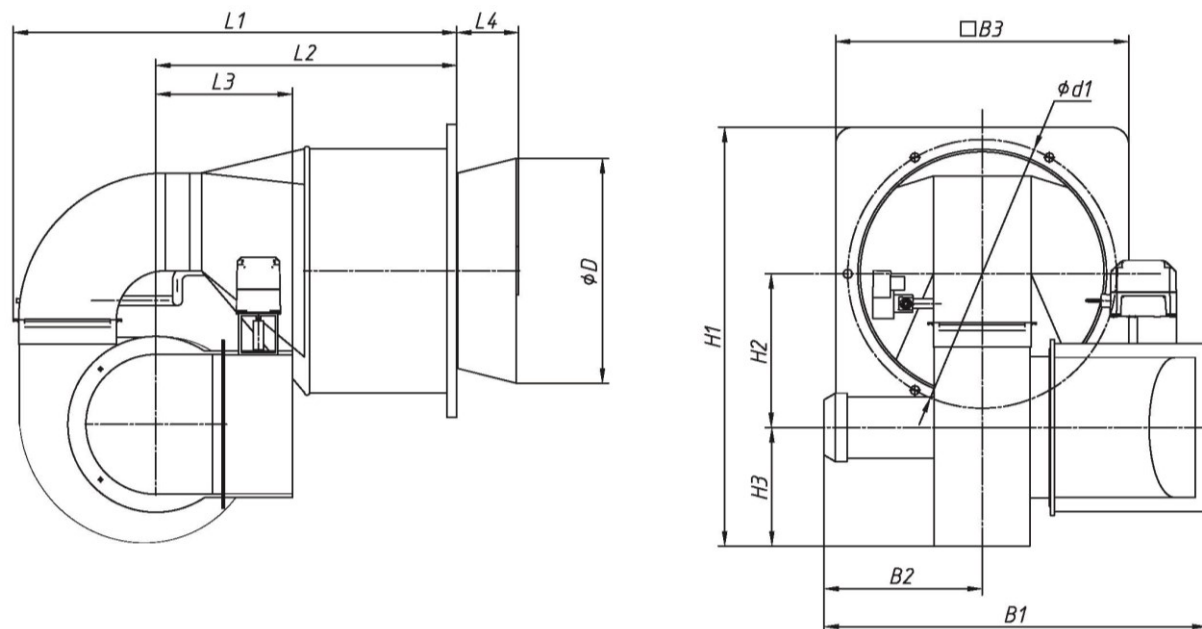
Габаритные и присоединительные размеры горелок ГЖБ-0,63...ГЖБ-10,9
